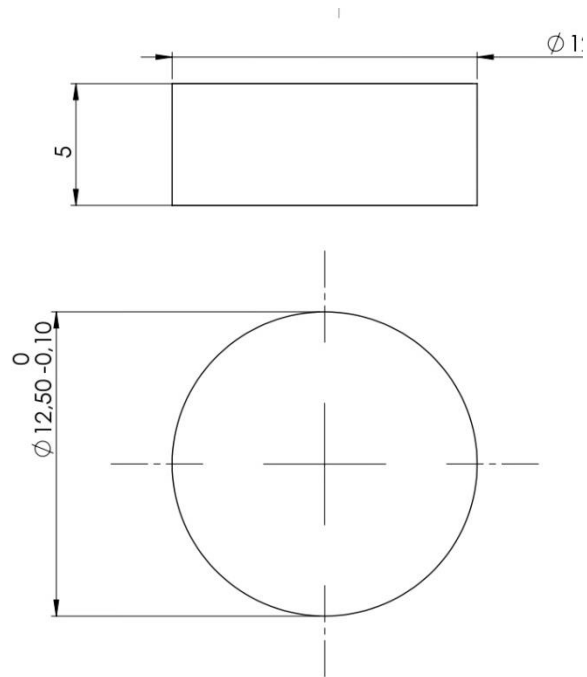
Desenho técnico da peça base do conjunto de prensagem.
